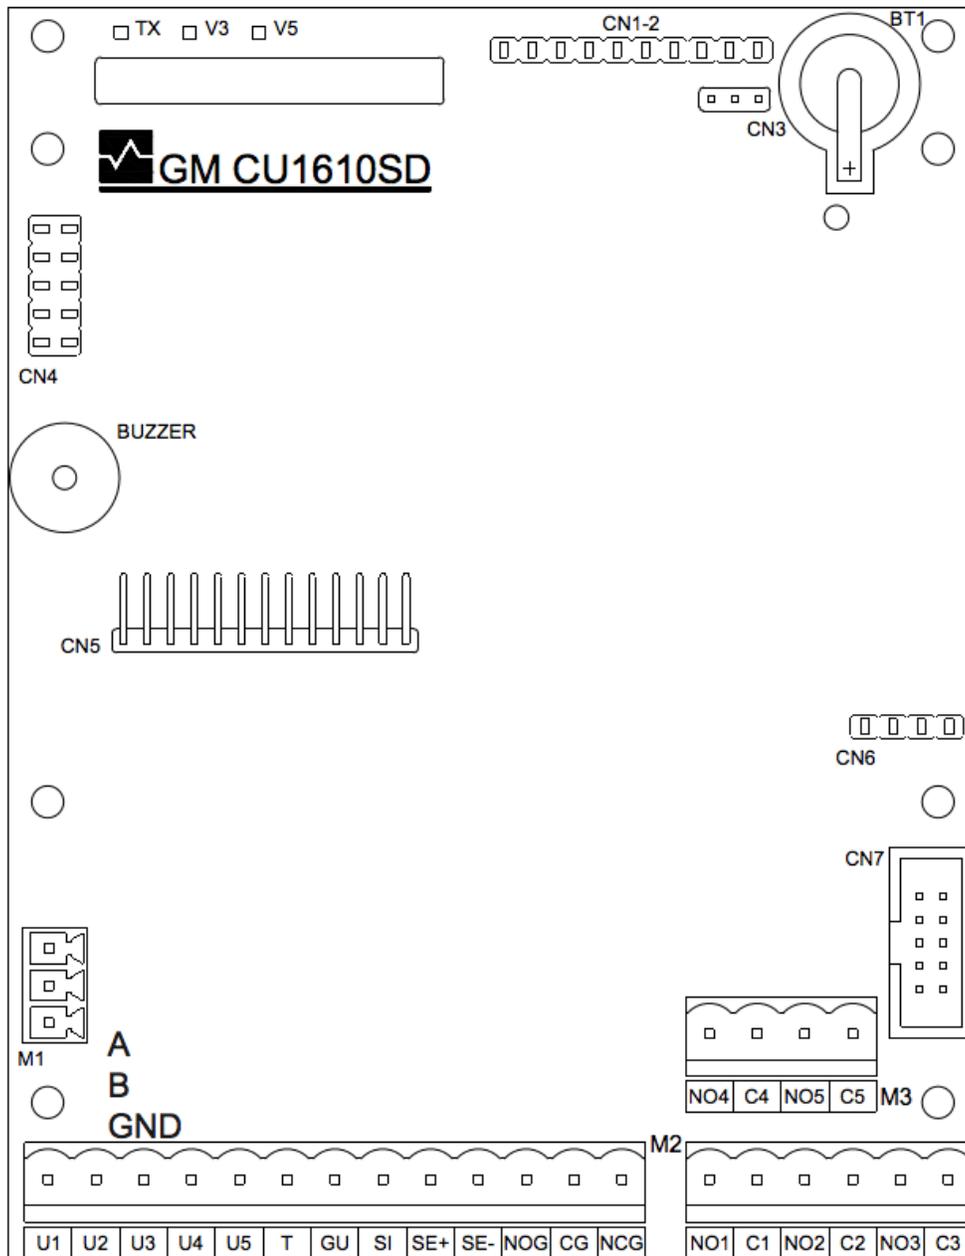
Lay-Out de la tarjeta madre del módulo GMCU1610SD.
